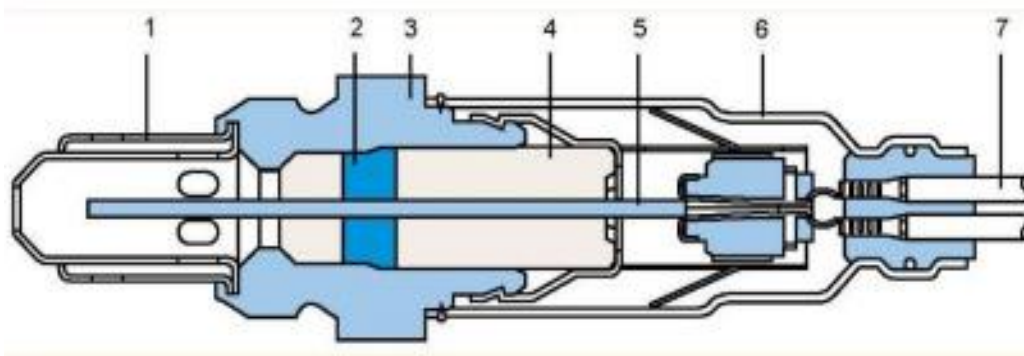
Планарний сенсор кисню [9]: 1 – трубка (захисна); 2 – керамічна вставка; 3 – корпус сенсора; 4 – утримувач керамічного типу; 5 – планарний чутливий елемент; 6 – трубчастий захист; 7 – контакти.
